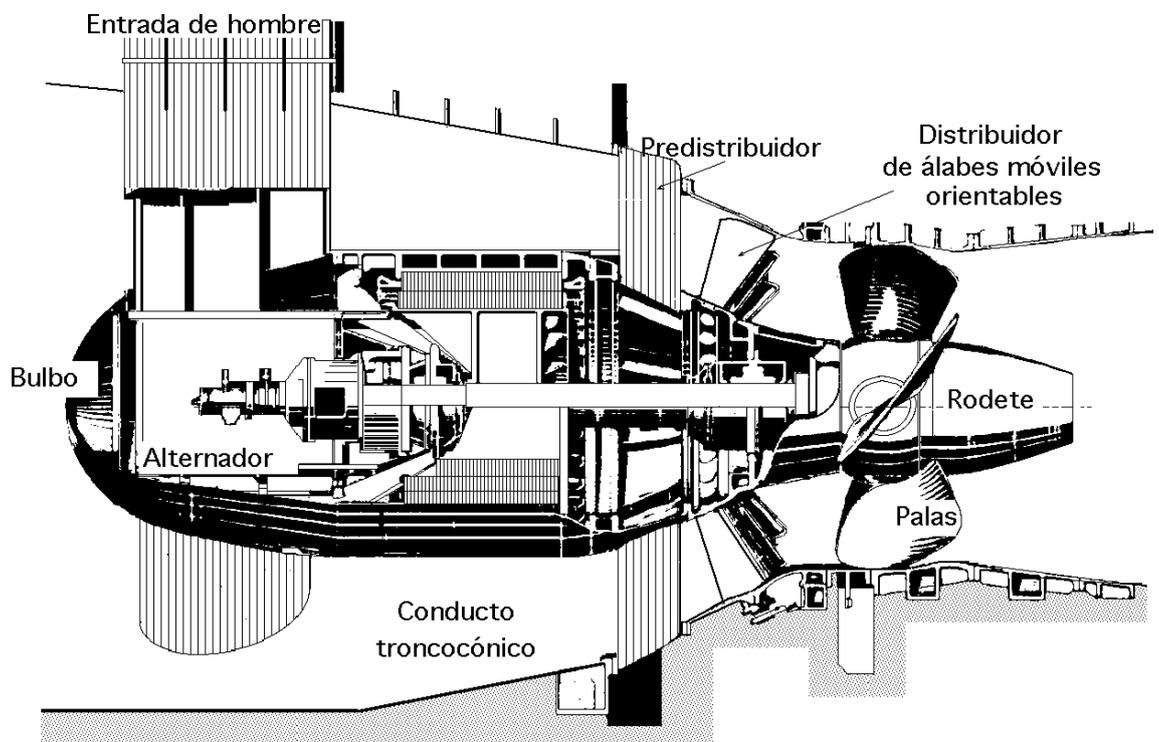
Esquema del montaje de una turbina tipo bulbo.
